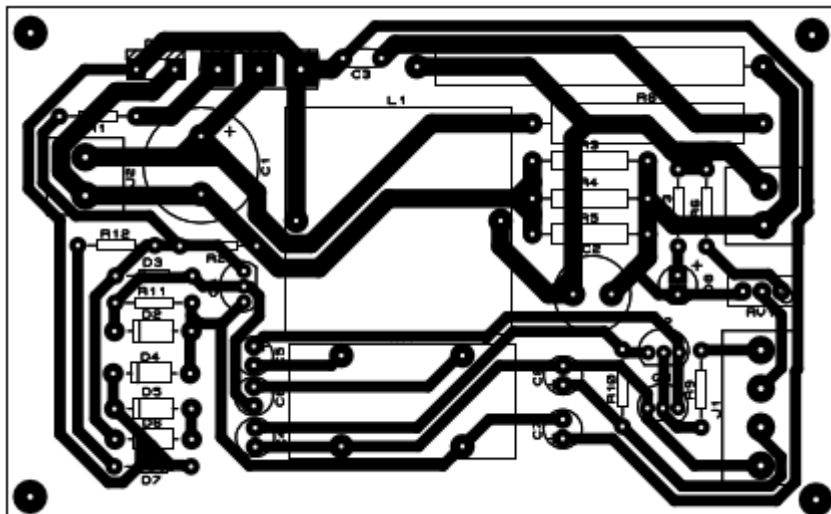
Layout da Placa de Circuito Impresso Conversor *Buck* + Circuito Driver
